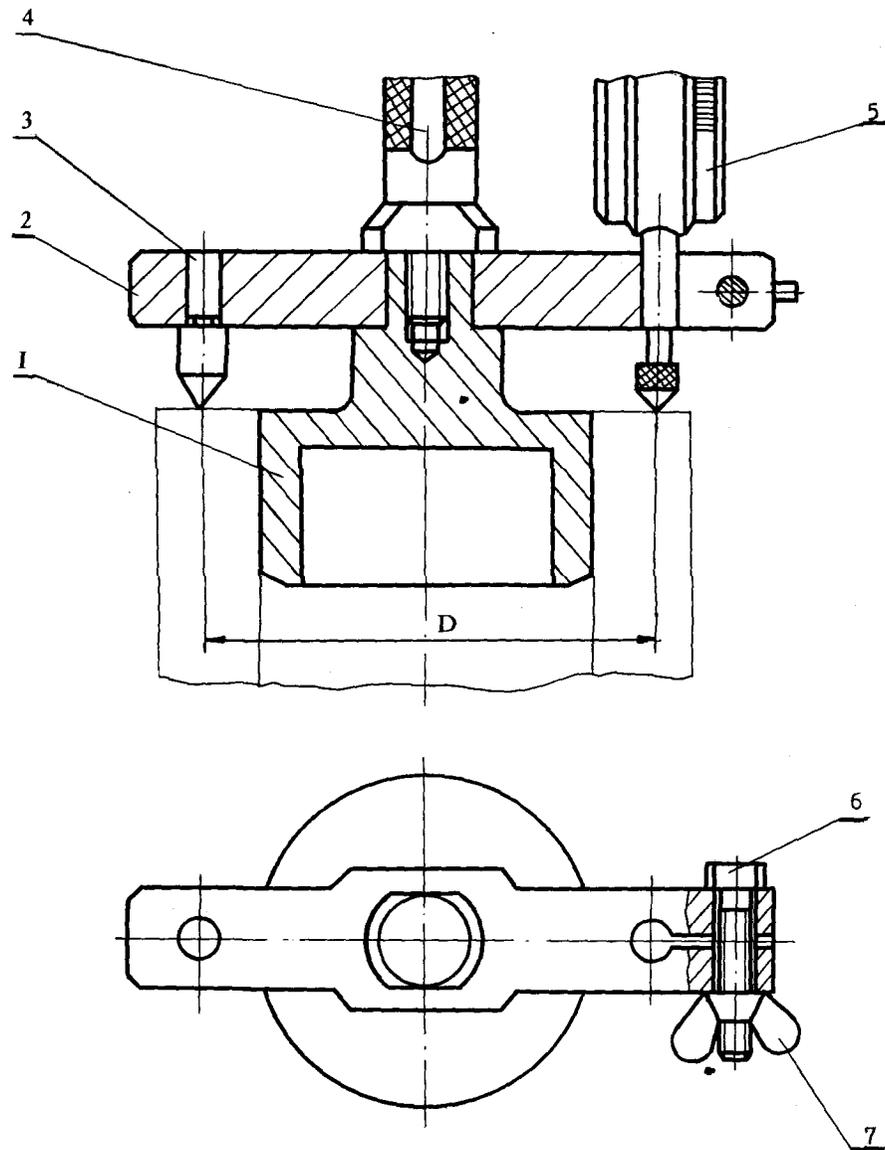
Съемное контрольное приспособление для проверки биения торца:
